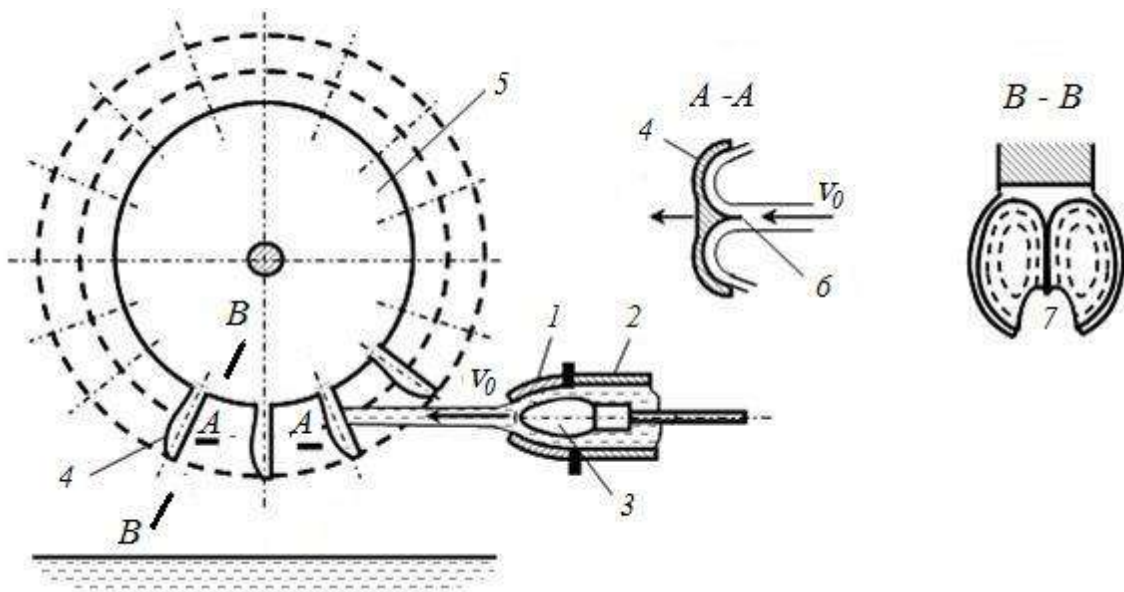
Схема ковшової турбіни: 1 – сопло; 2 – напірний водовод; 3 – регулювальна голка; 4 – лопатка; 5 – робоче колесо; 6 – ніж лопатки; 7 – прорізь
